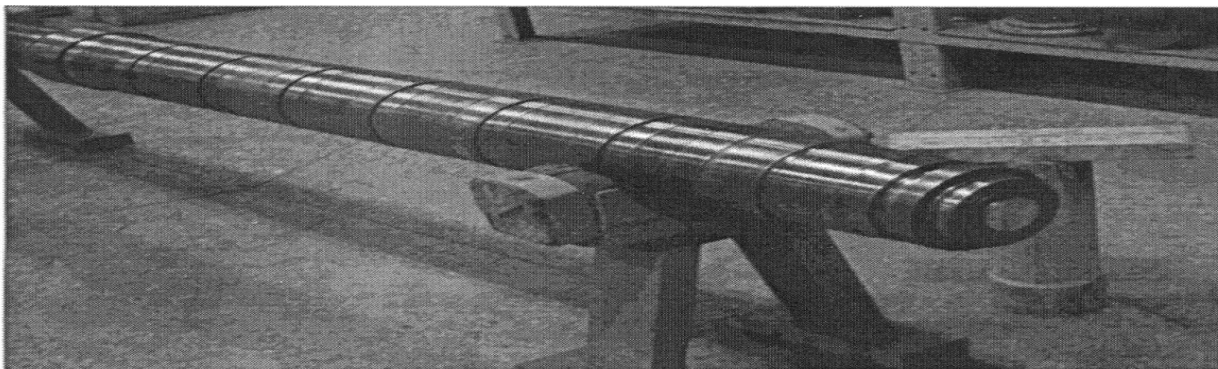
Корпус уплотнения и вал с усталостной трещиной
